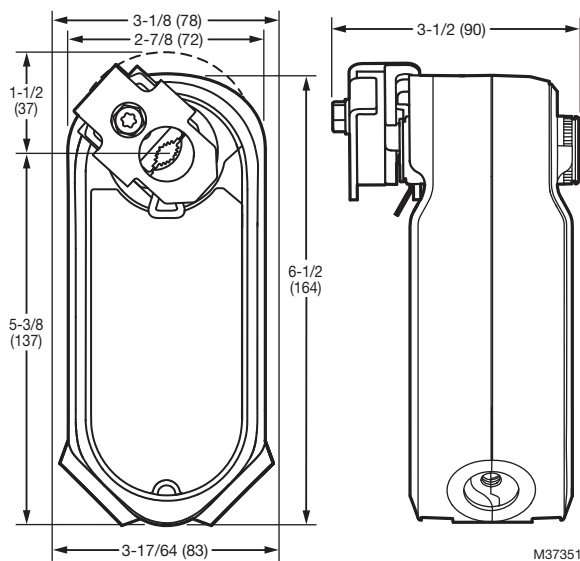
Zeichnung des Aktuators ohne Durchführung mit Abmessungen in Zoll (mm).
